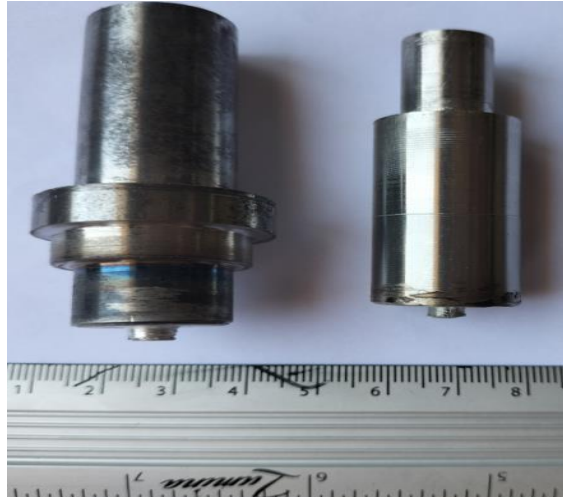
Les outils de soudage de FSW utilisé.
